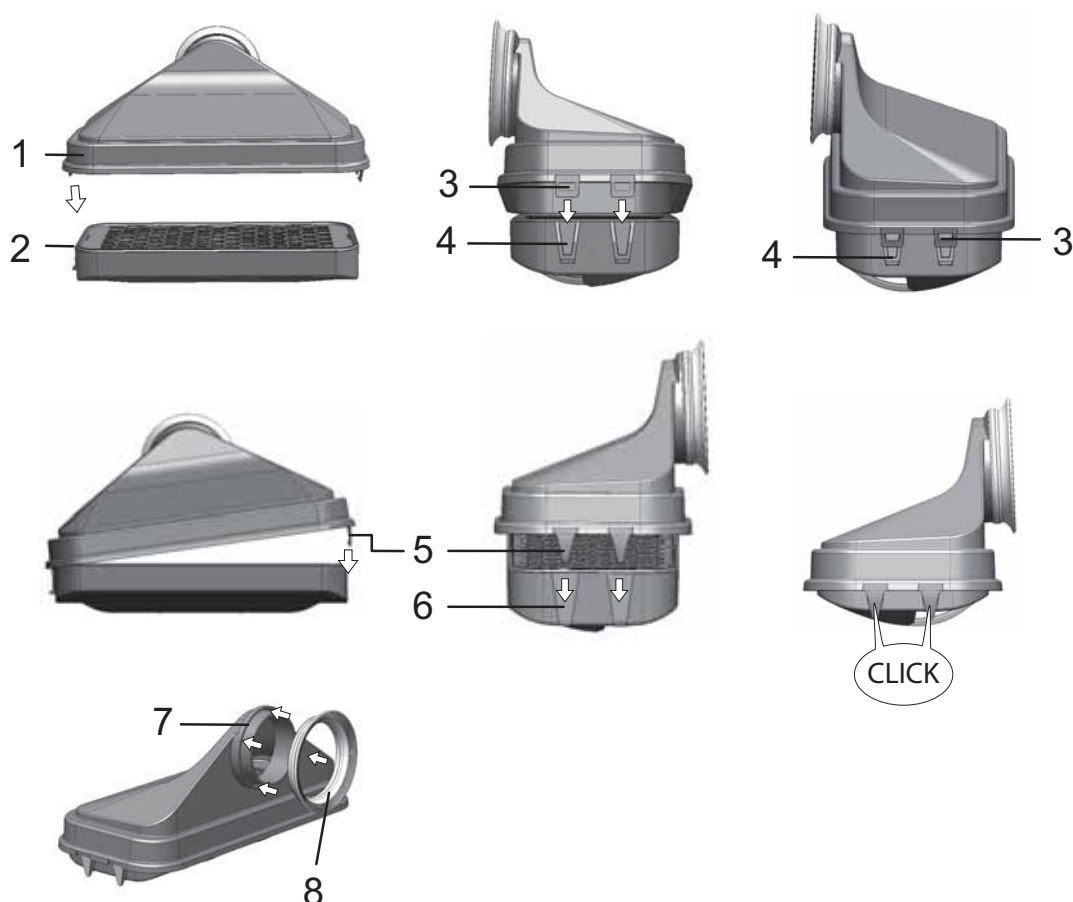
Assembler le filtre HEPA et le boîtier de filtre à air
